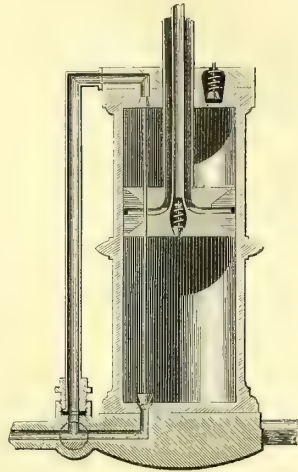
Machine pneumatique de Bianchi; vue intérieure du corps de pompe.
